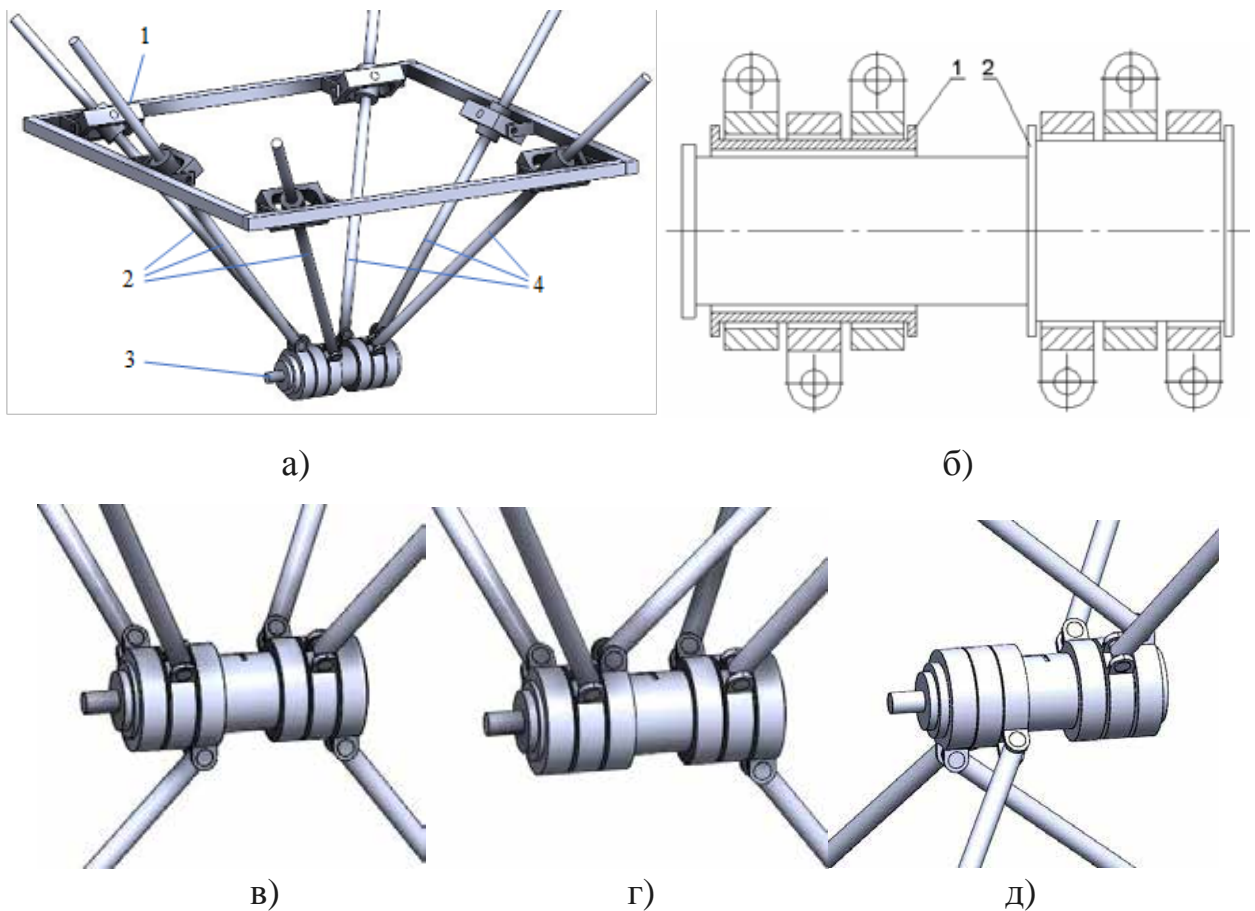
Багатокоординатний верстат з надлишковим приводом: а) компоновка, б) робочий орган; в), г), д) варіанти розміщення штанг з шарнірами на робочому органі
